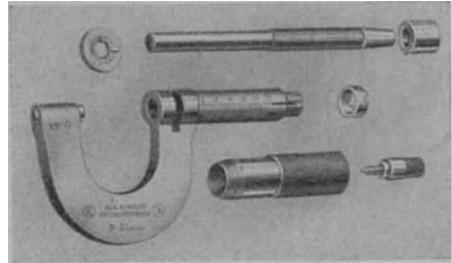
Mikrometer mit Gefühlschraube, zerlegt. Aug. Kirsch, Aschaffenburg.
